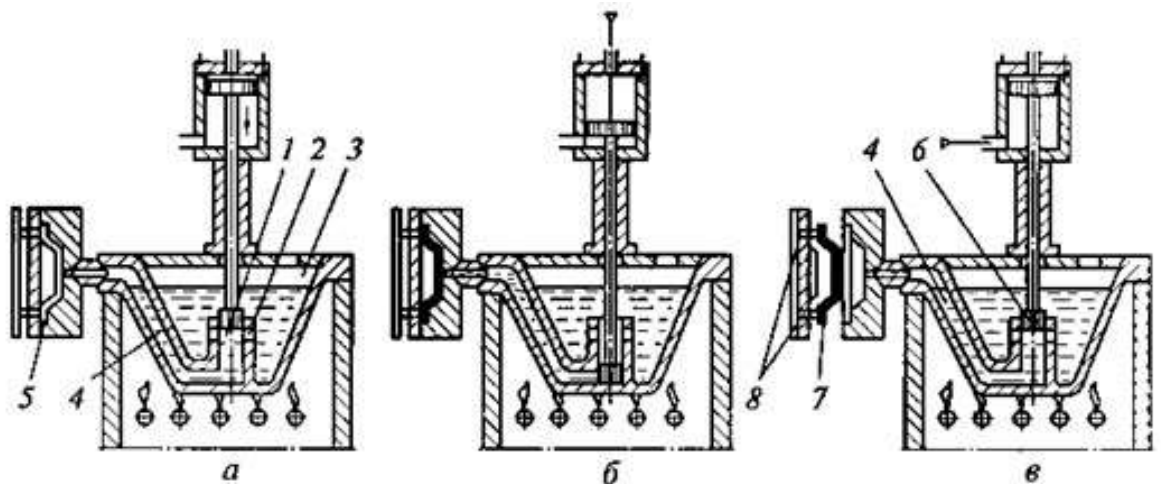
Лиття під тиском 1 – рідкий метал; 2 – зона ходу поршня; 3 – ванна з металом; 4 – ливарний канал; 5 – порожнина форми; 6 – поршень; 7 – виливок; 8 – форма.
